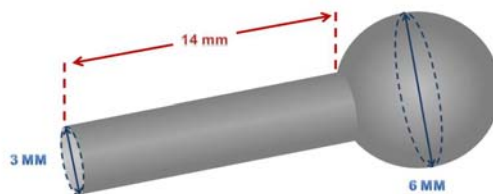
Dimensões do corpo de prova em Milímetros (MM)
